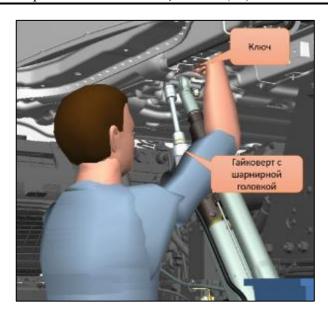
Процесс затяжки гидроцилиндра ключом и гайковертом с шарнирной головкой
